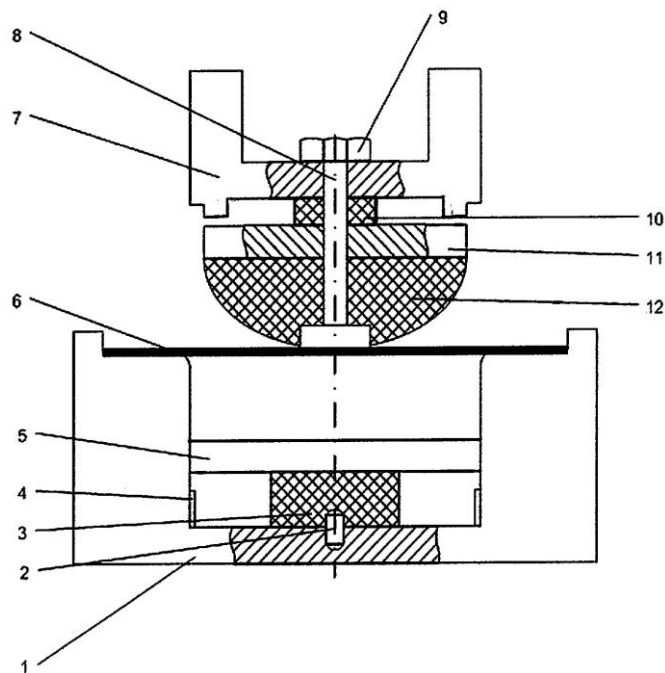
Схема штампа для изгиба листовых деталей: 1 – матрица;
